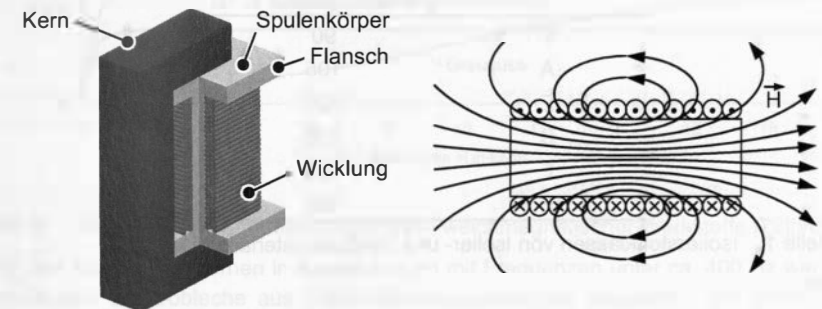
Prinzipieller Aufbau eines wickeltechnischen Produkts (links); magnetische Feldlinien in einer Zylinderspule [72] (rechts)
